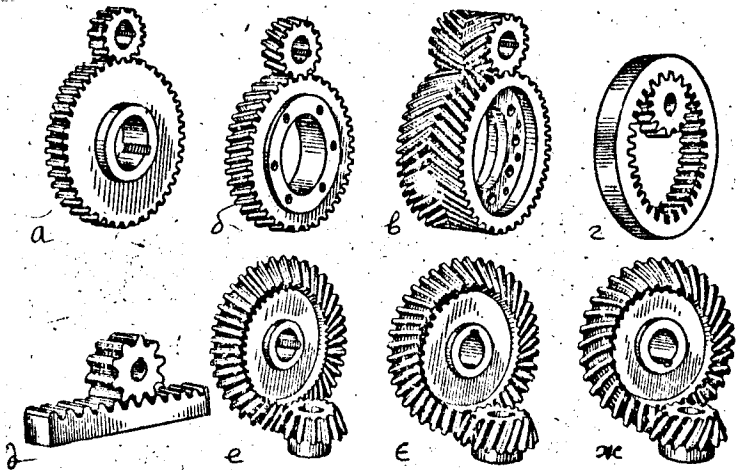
Основні типи зубчастих передач: а - циліндрична прямозуба; б - циліндрична косозуба; в - шевронна; г - з внутрішнім зачепленням; д - рейкова; е - конусна прямозуба; е - конусна косозуба; ж - конусна з коловими зуб'ями
